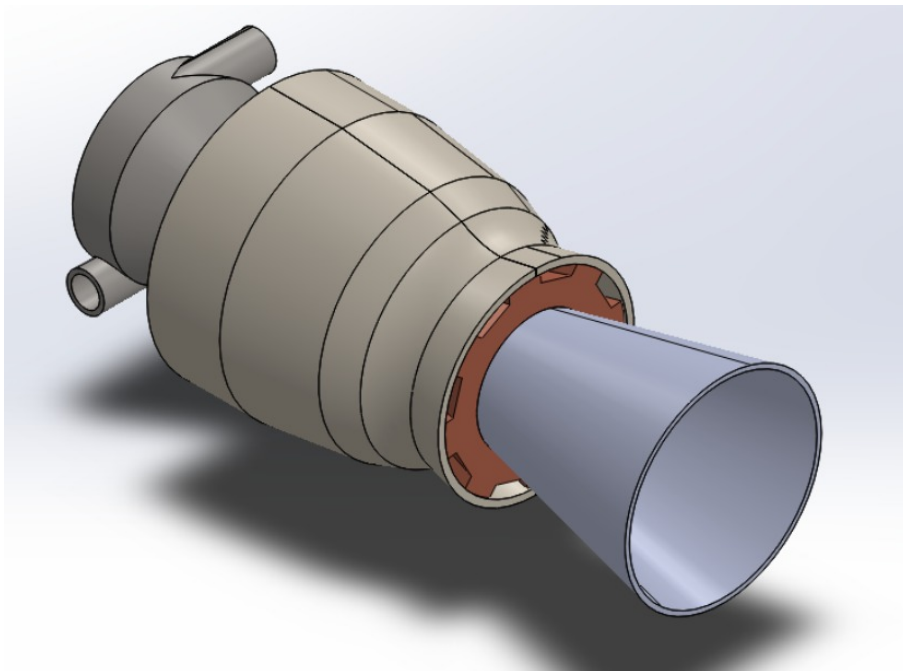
Vista do motor exibindo a parede externa de Inconel 625.
